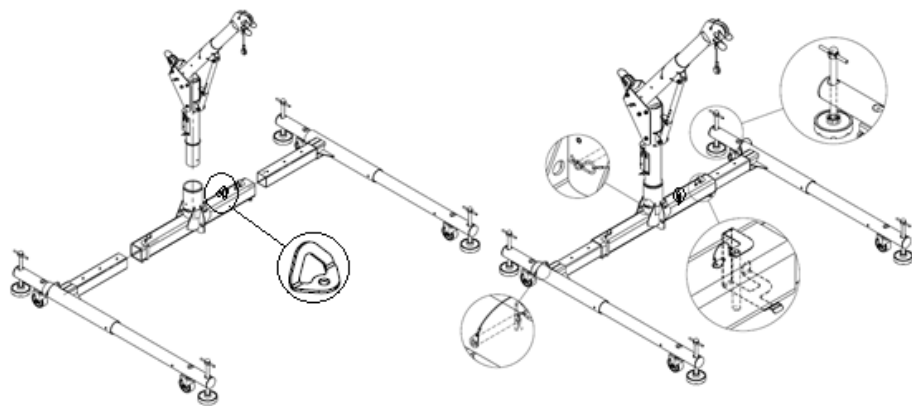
Монтаж СОБ Кран Е11-1L
